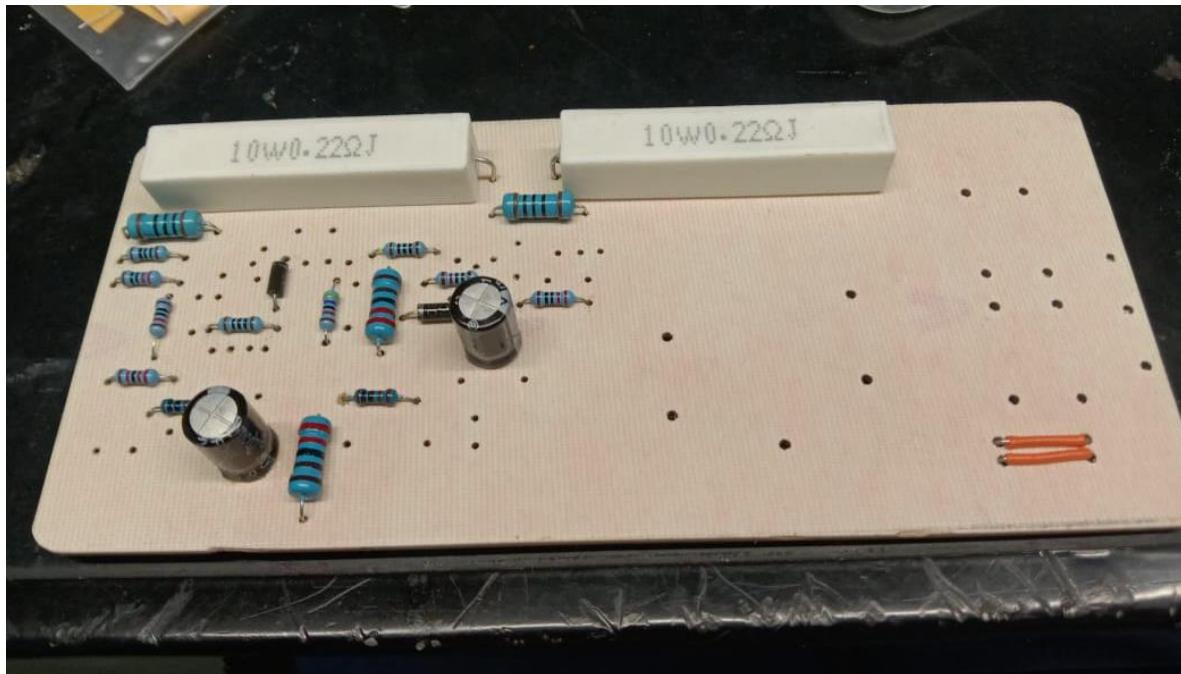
Segundo grupo de componentes soldados a la PCB.
